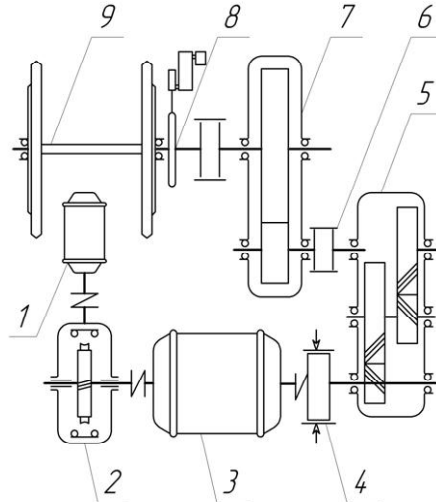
Схема ПГТЭ ЭМ-4: 1 – вспомогательный электродвигатель; 2 – редуктор вспомогательного электродвигателя; 3 – главный электродвигатель; 4 – рабочие тормоза; 5 – быстроходный редуктор; 6 – зубчатые муфты; 7 – тихоходный редуктор; 8 – реле оборотов с приводом; 9 – главный вал с тяговыми звездочками и аварийными тормозами
